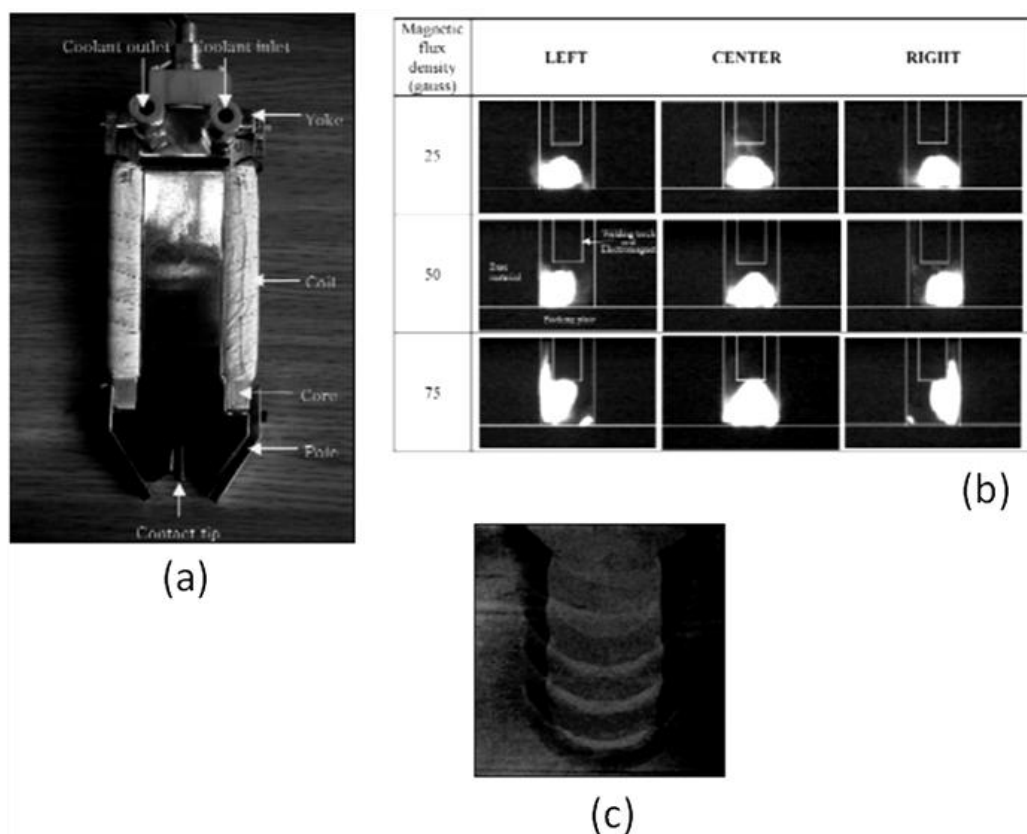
Efeitos da Oscilação magnética em chanfro profundo. (a) tocha de soldagem, (b) movimentação do arco, (c) sobreposição de cordões.
